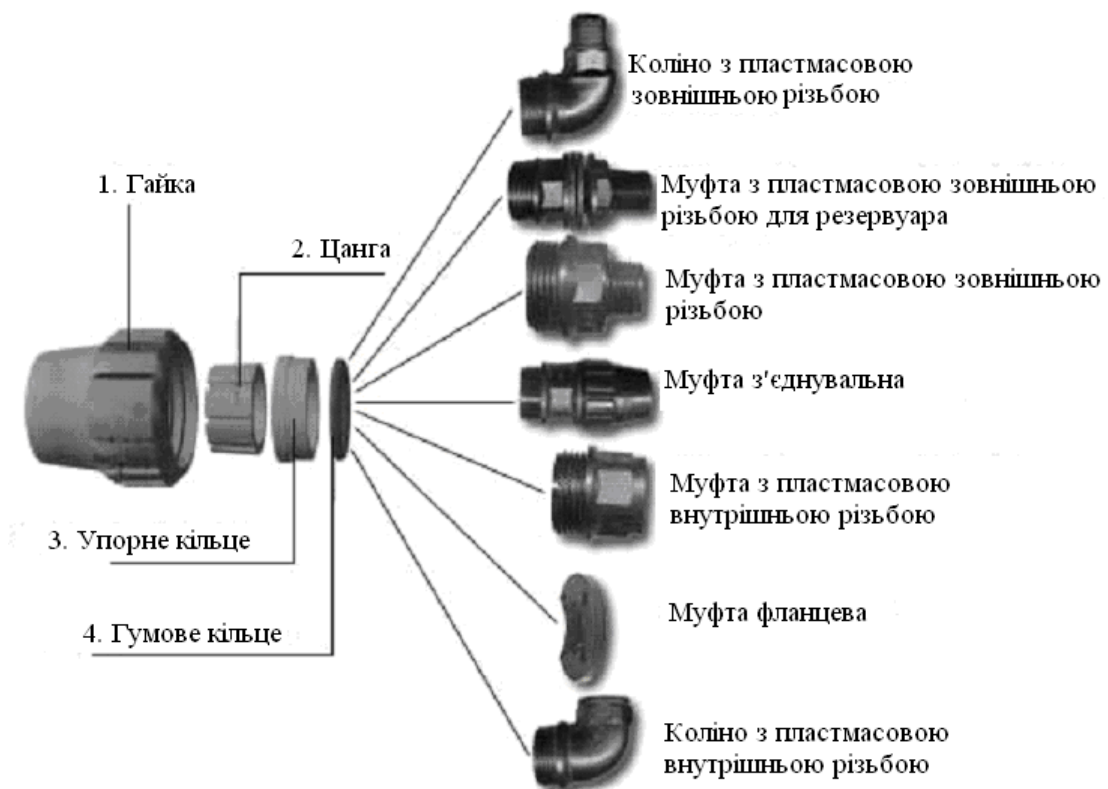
Схема різноманітного фітингового з'єднання. Матеріал гайки і корпусу – поліпропілен; цанги, упорного кільця – поліфенілоксид
